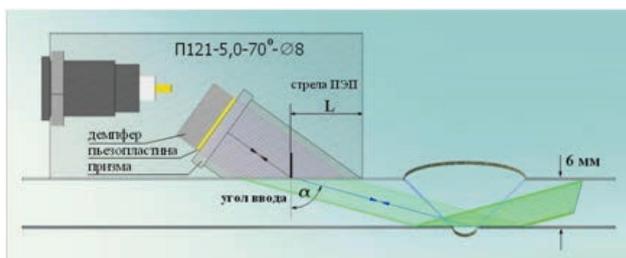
Прозвучивание корня сварного соединения наклонным совмещенным преобразователем
